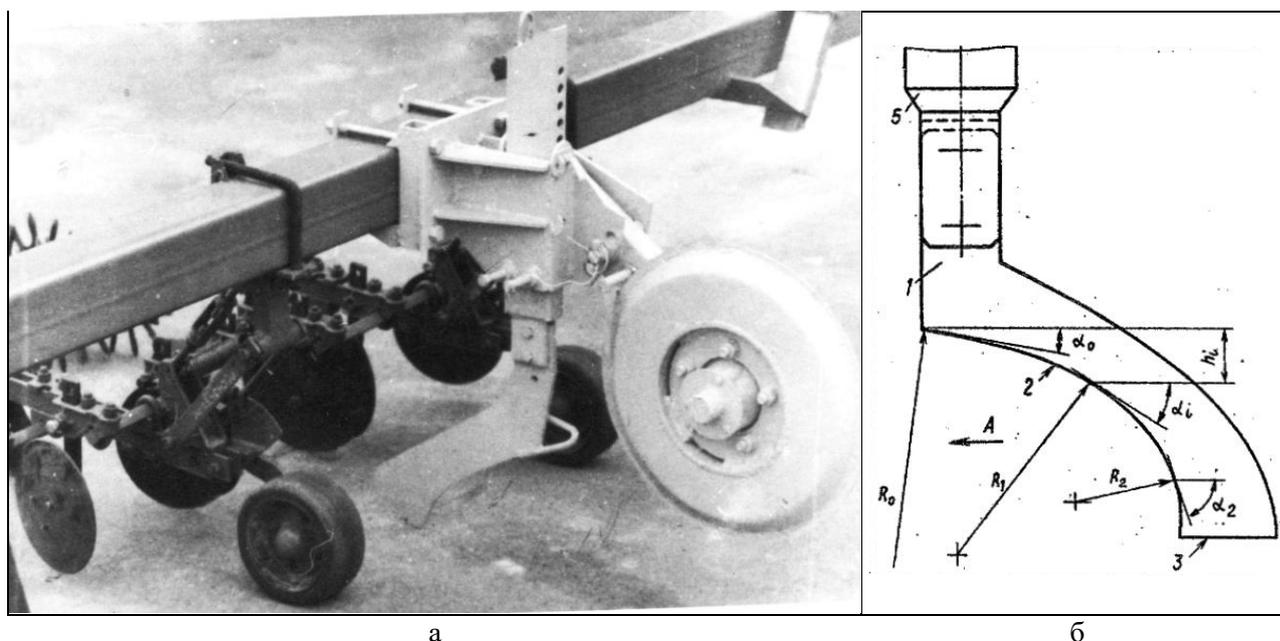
Вид ориентатора пропашных машин, разработки НПО «Сахарная свекла»: а - конструктивное исполнение для культиватора «Плай»; б - форма ножа для образования щелей в почве [15]
